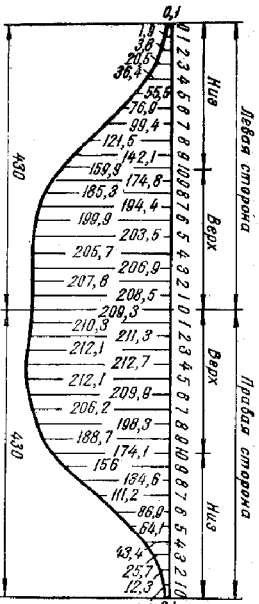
Развертка конуса отрезка сварного тройника.
